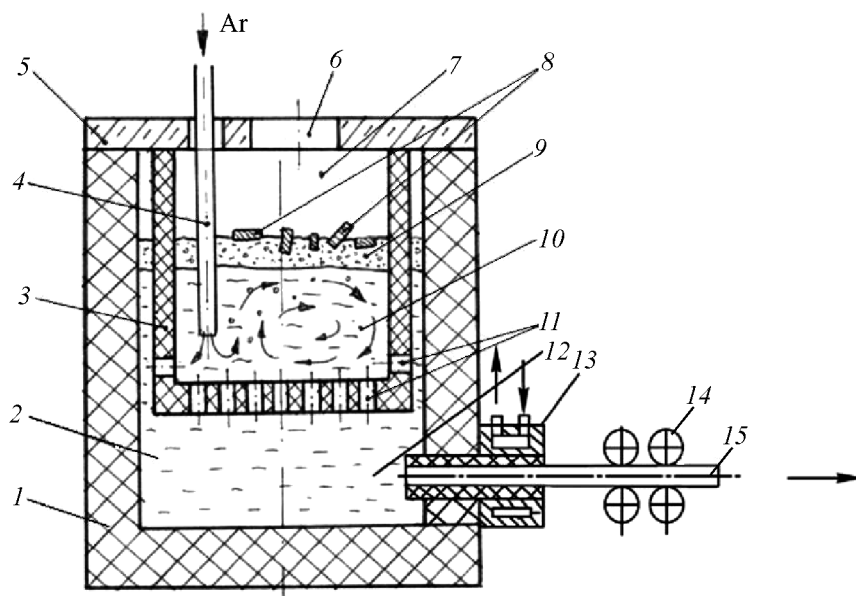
Устройство агрегата для непрерывной плавки и литья заготовок
